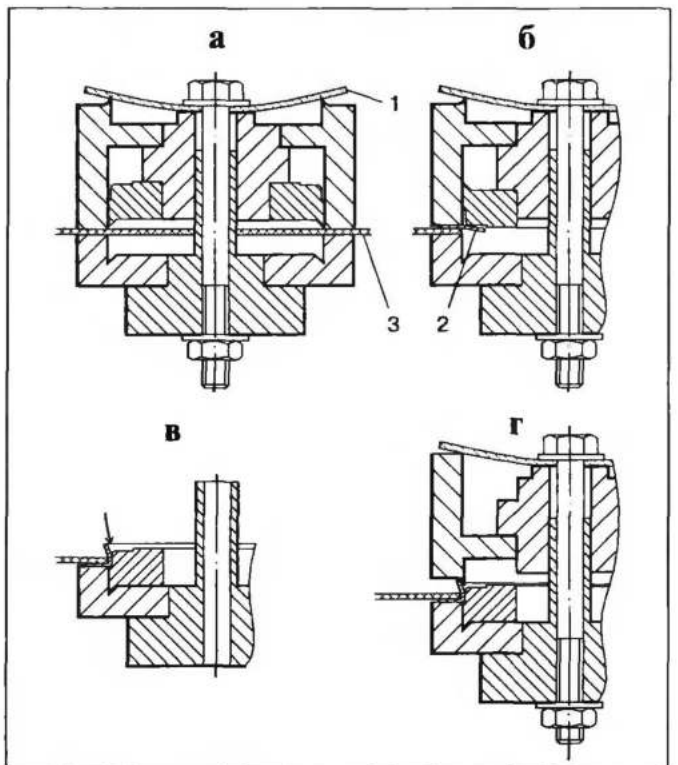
Схема работы простого приспособления для окантовки отверстий прокладок: а — резка отверстия в прокладке; б — предварительная гибка окантовки; в — отгибание края окантовки; г — окончательная вальцовка окантовки; 1 — тарельчатая пружина; 2 — окантовка; 3 — прокладка
